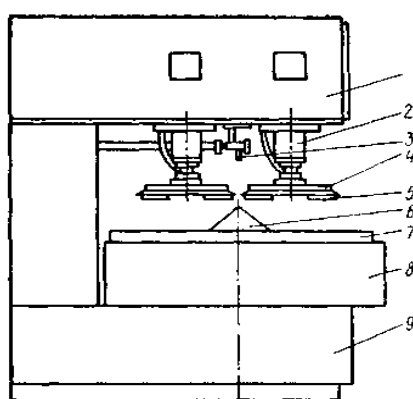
Напівавтомат для хіміко-механічної поліровки [13]
